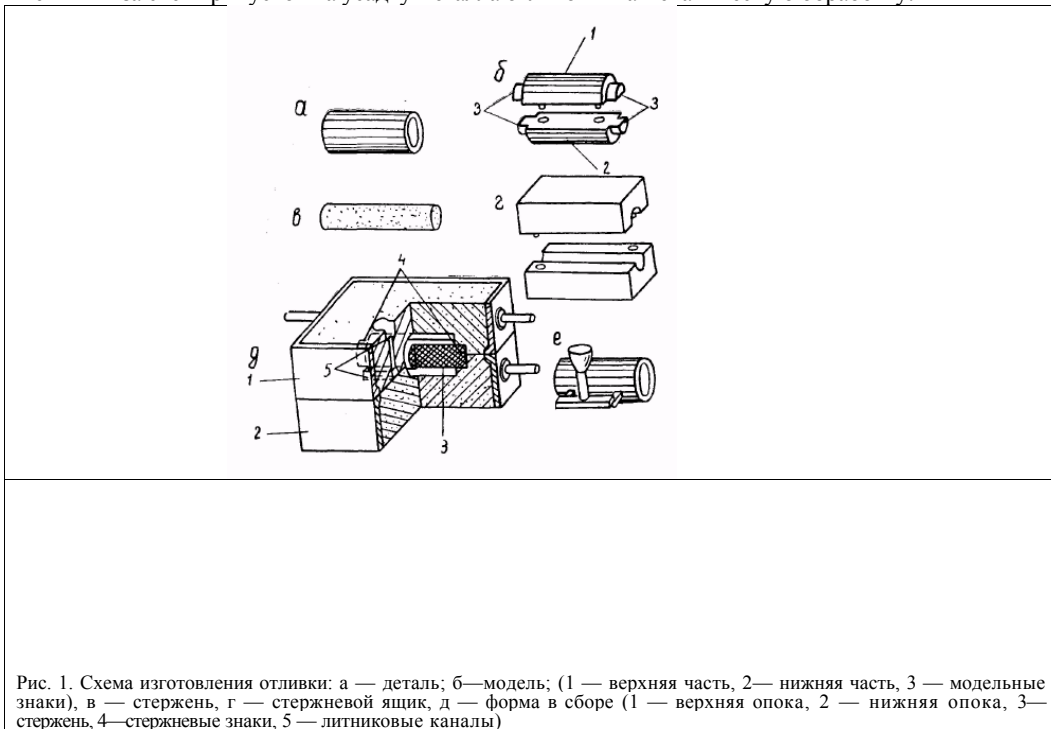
Схема изготовления отливки: а — деталь; б—модель; (1 — верхняя часть, 2— нижняя часть, 3 — модельные знаки), в — стержень, г — стержневой ящик, д — форма в сборе (1 — верхняя опока, 2 — нижняя опока, 3— стержень, 4—стержневые знаки, 5 — литниковые каналы)
